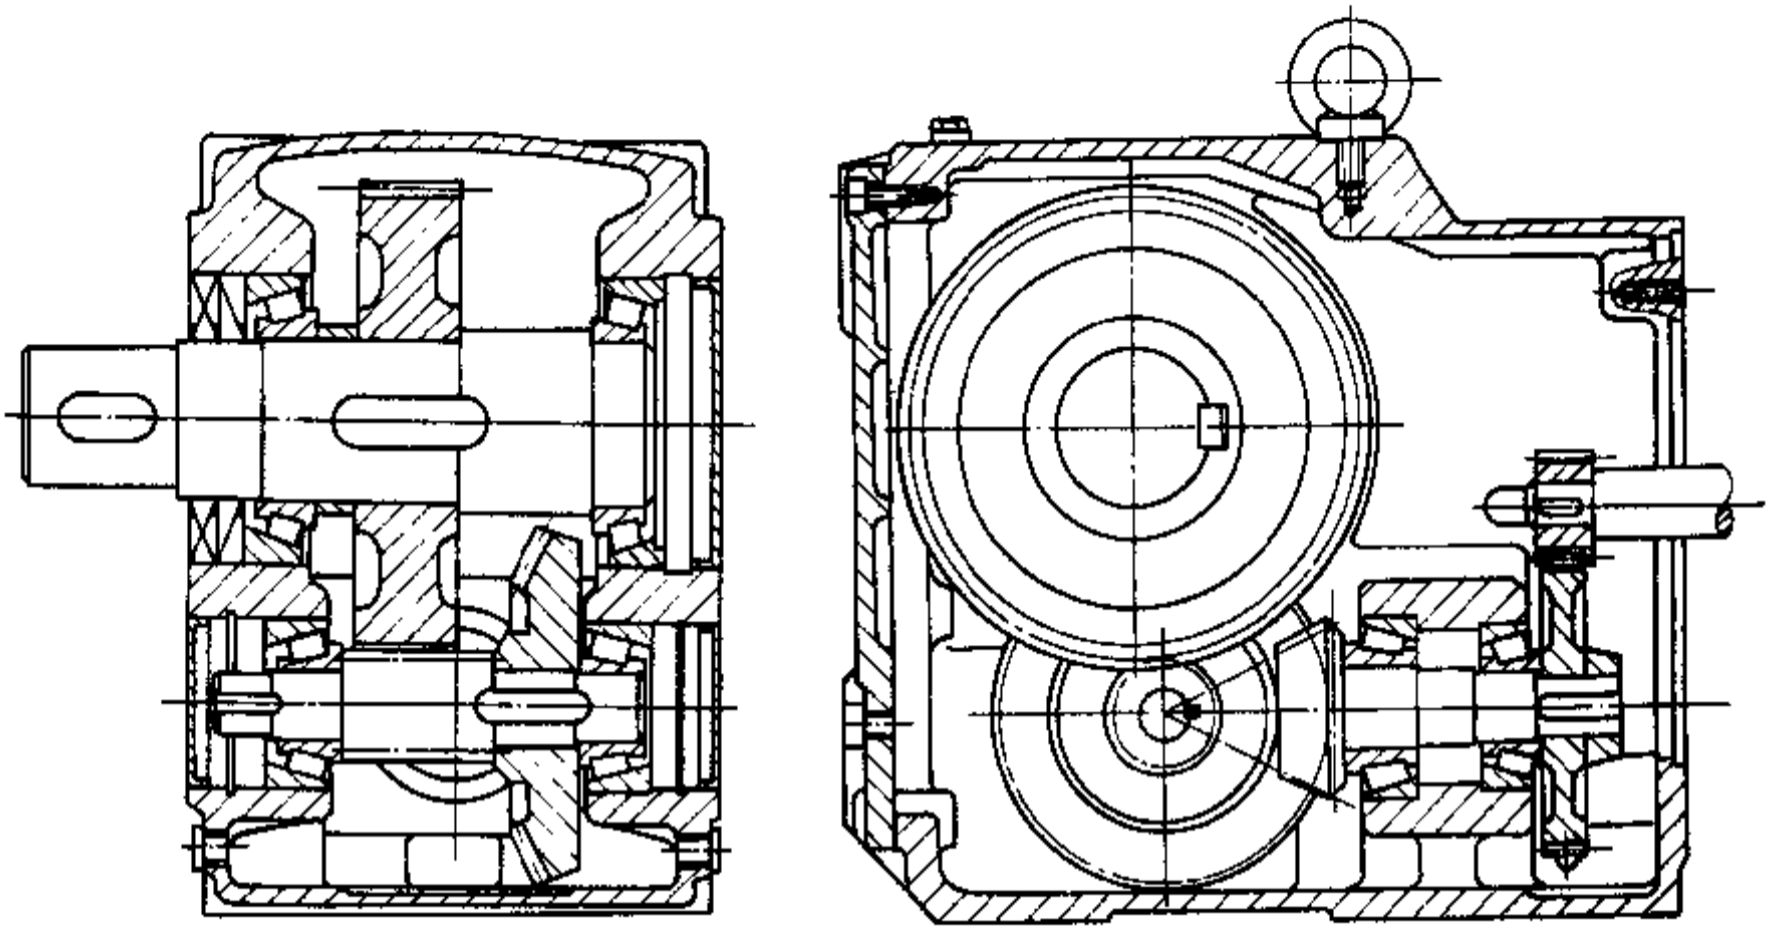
圆柱齿轮-圆锥齿轮-圆柱齿轮三级减速器
